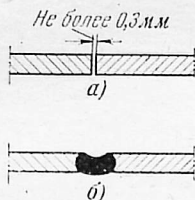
Аргон-дуговая вакуумная сварка встык оплавлением кромок основного металла.
